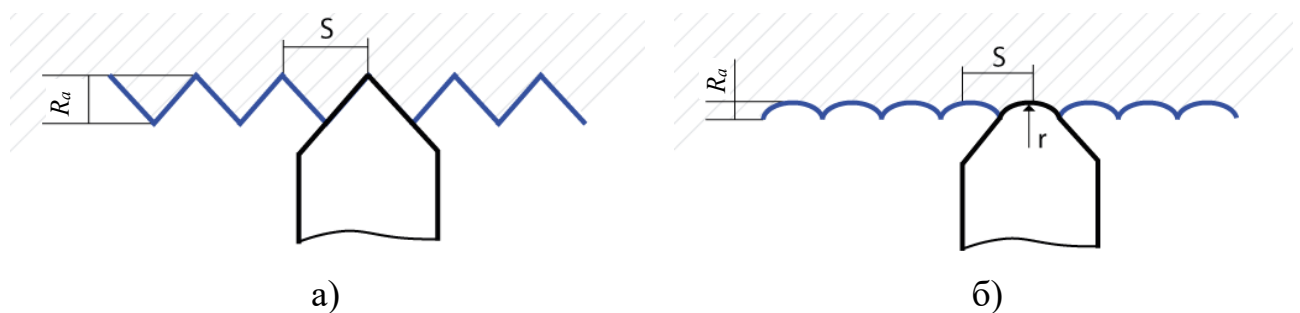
Влияние величины округления режущей кромки на шероховатость поверхности, где: а) острая кромка, б) закругленная кромка
